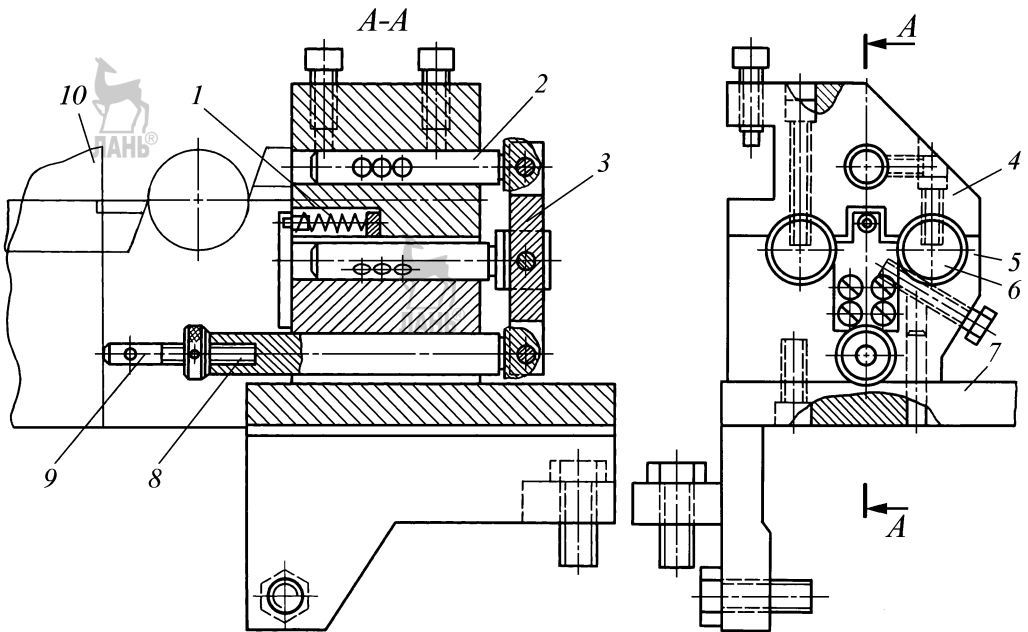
Приспособление для двустороннего нарезания резьб:
